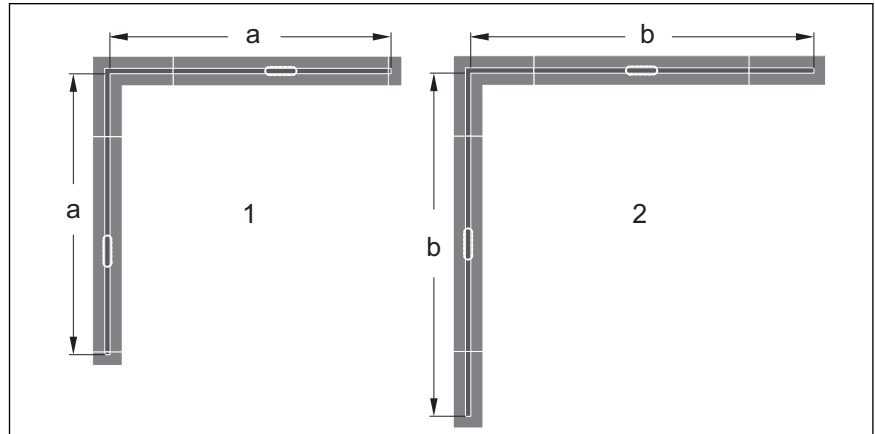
Opciones de montaje con piezas de unión de 90° para variante en L
